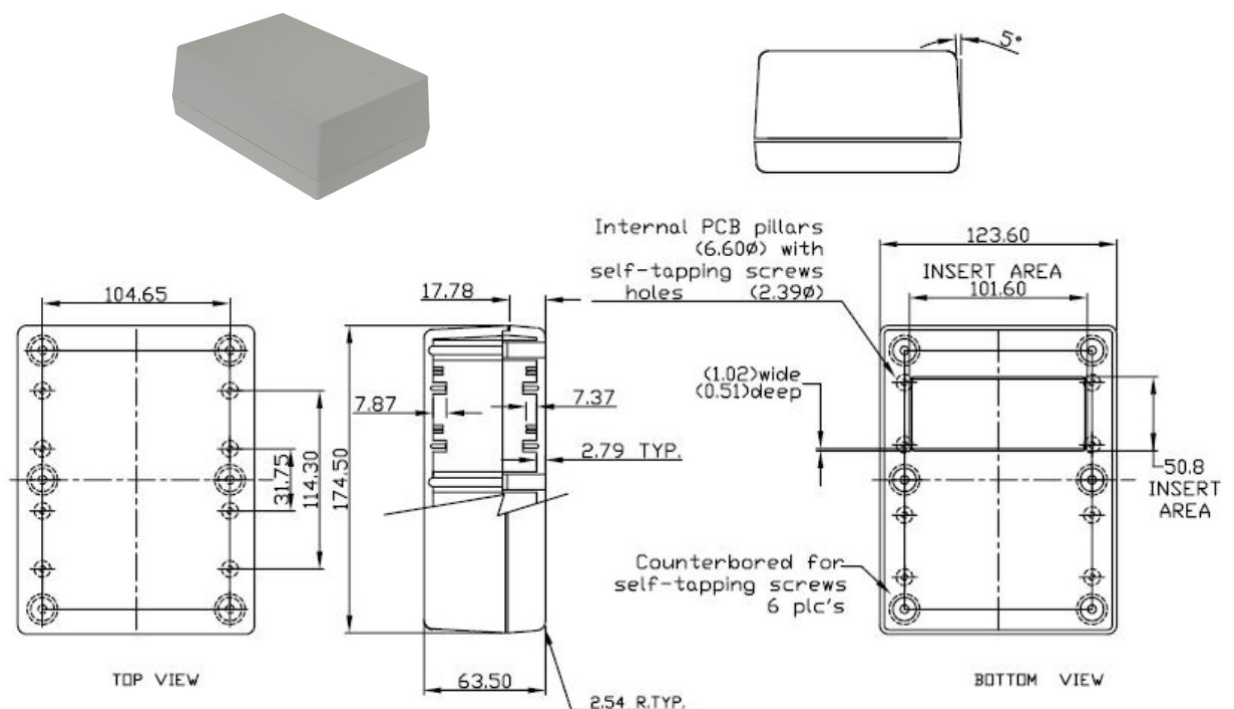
Корпус «GAINTA 1213» в сборе с нижней крышкой
